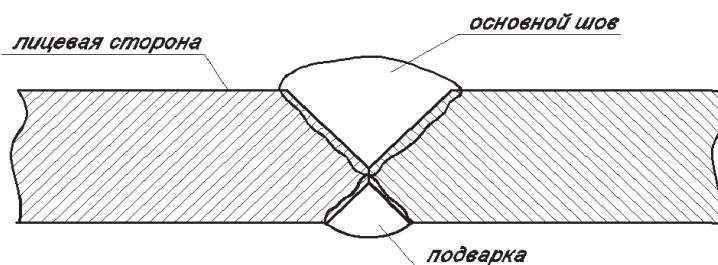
Сварной шов с несимметрично подготовленными кромками
